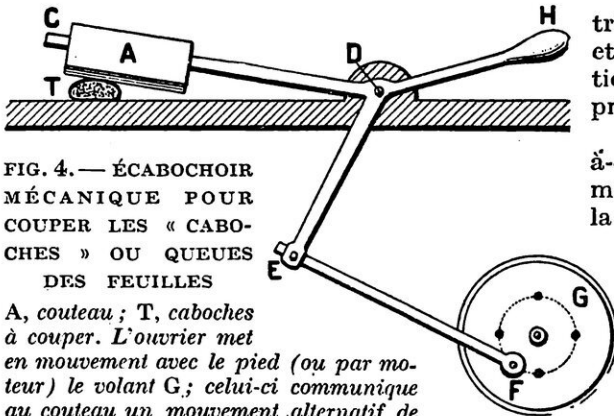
ÉCABOCHOIR MÉCANIQUE POUR COUPER LES « CABOCHES » OU QUEUES DES FEUILLES
